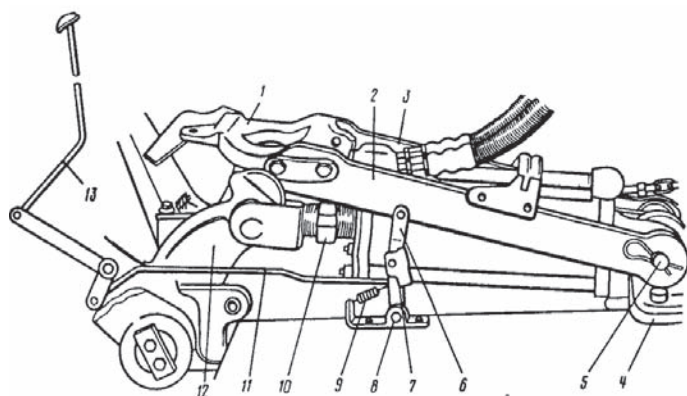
Механизм фиксации навесного устройства. 1 — захват; 2 и 3 — щеки; 4 — кронштейн гидроцилиндра; 5 — ось; 6 и 7 — рычаги; 8 — кронштейн; 9 — пружина; 10 — упор; 11 — тяга управления; 12 — поворотный рычаг; 13 — рукоятка управления
